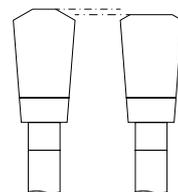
Smusso trapezoidale piatto (TR-F-Fa)
